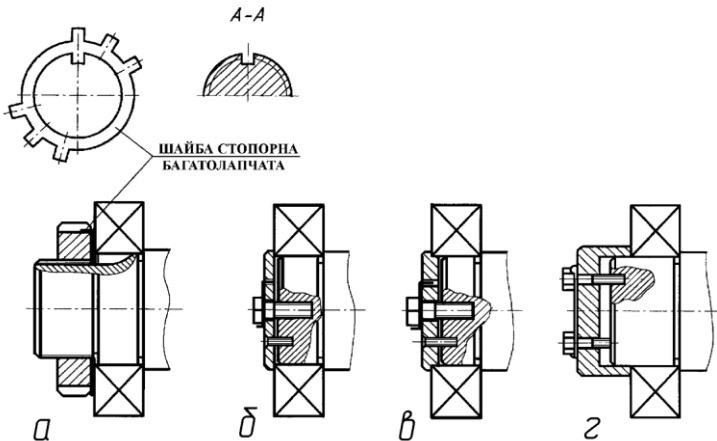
8. Способи кріплення підшипників: а - шліцьовою гайкою і багатолапчастою стопорною шайбою; б - торцевою шайбою; в - центрування відносно отвору підшипника; г - центрування підшипника по валу
